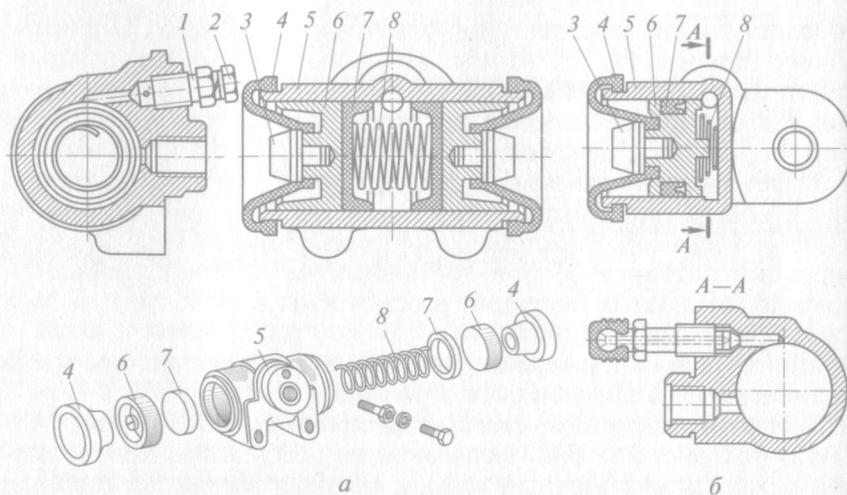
Колесные тормозные цилиндры гидропривода тормозных механизмов:
